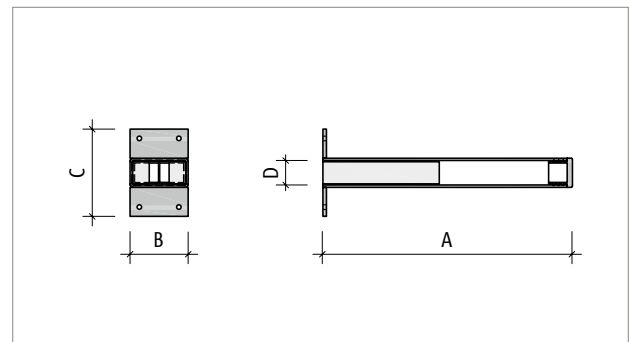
Schöck Stacon® type LD-Q part S: Dimensions of the transversely movable sleeve
